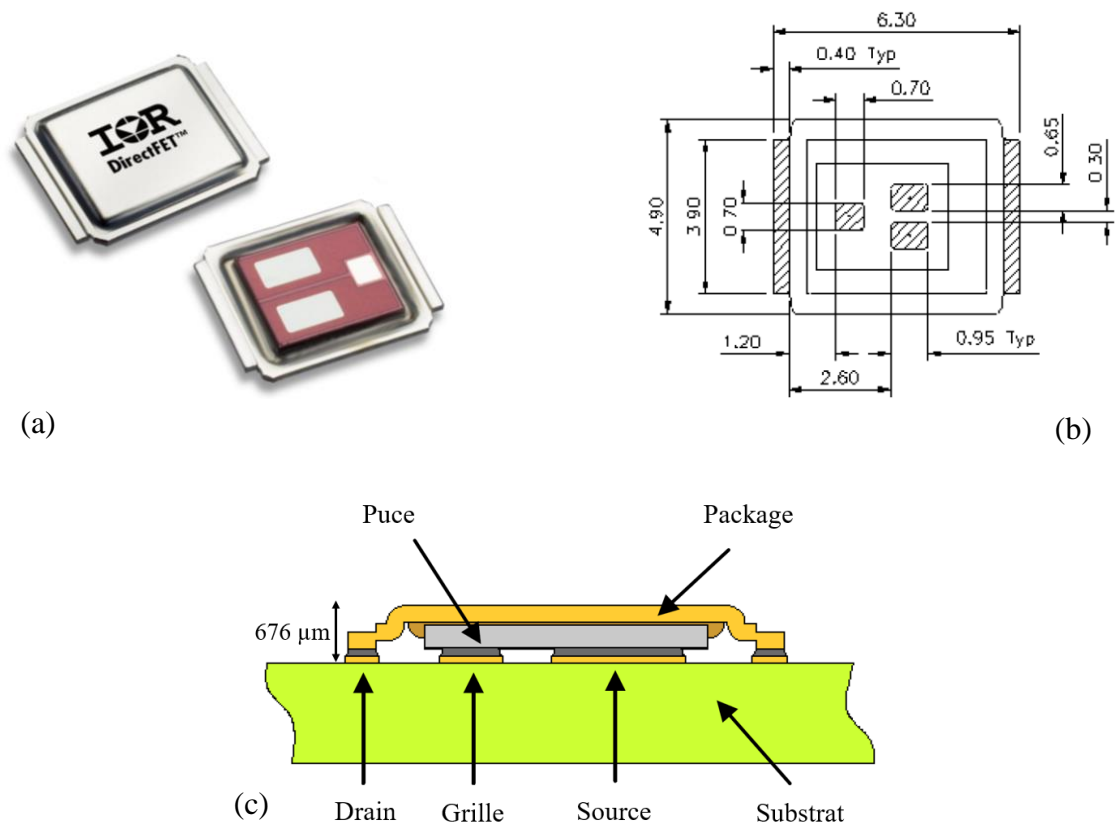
MOSFET IRF6775MTRPbF (a) photographie du boîtier DirectFET MZ (b) Vue de dessous et dimensions (c) Coupe transversale
